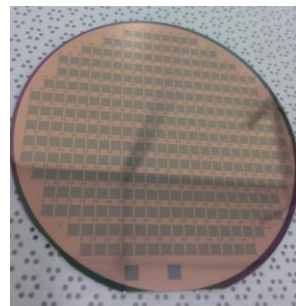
Внешний вид пластины со сформированными контактными площадками
